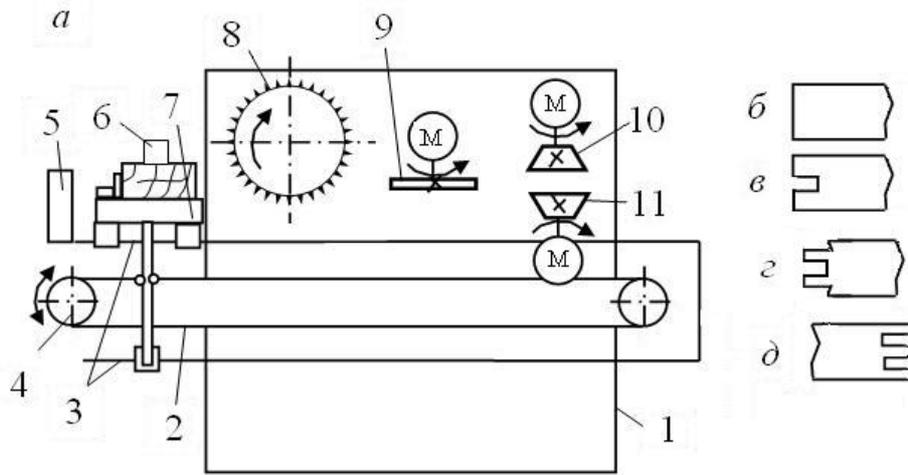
Односторонний рамный шипорезный станок ШО15Г-5:
